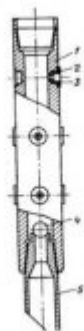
Гидропескоструйный перфоратор: 1 - корпус; 2 - держатель; 3 - струйная насадка; 4 - шаровой клапан; 5 - направляющая насадка
